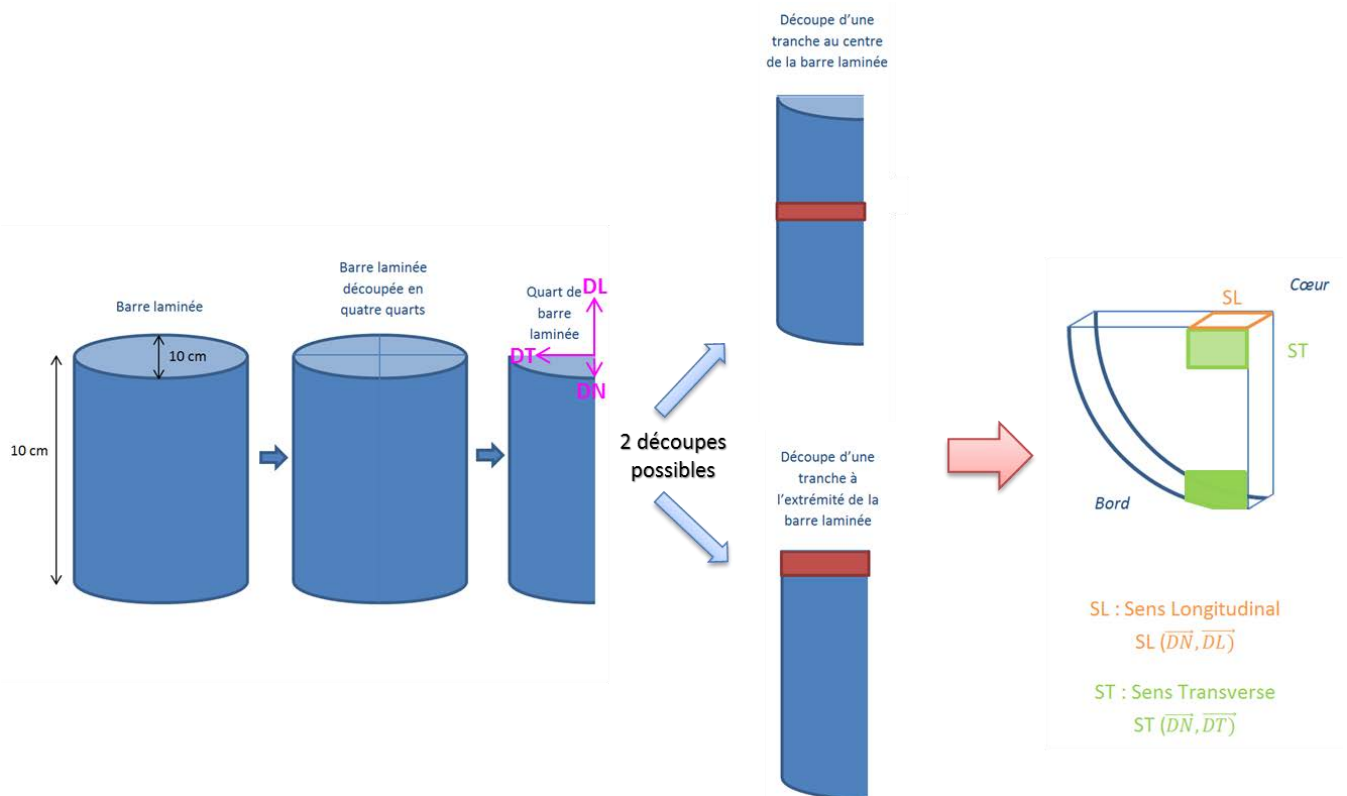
Plans de découpe des barres laminées des alliages T40 et TA6V.
